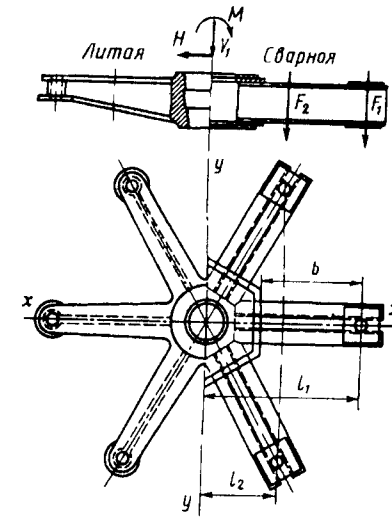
Схема фундаментной плиты крана с неподвижной колонной
